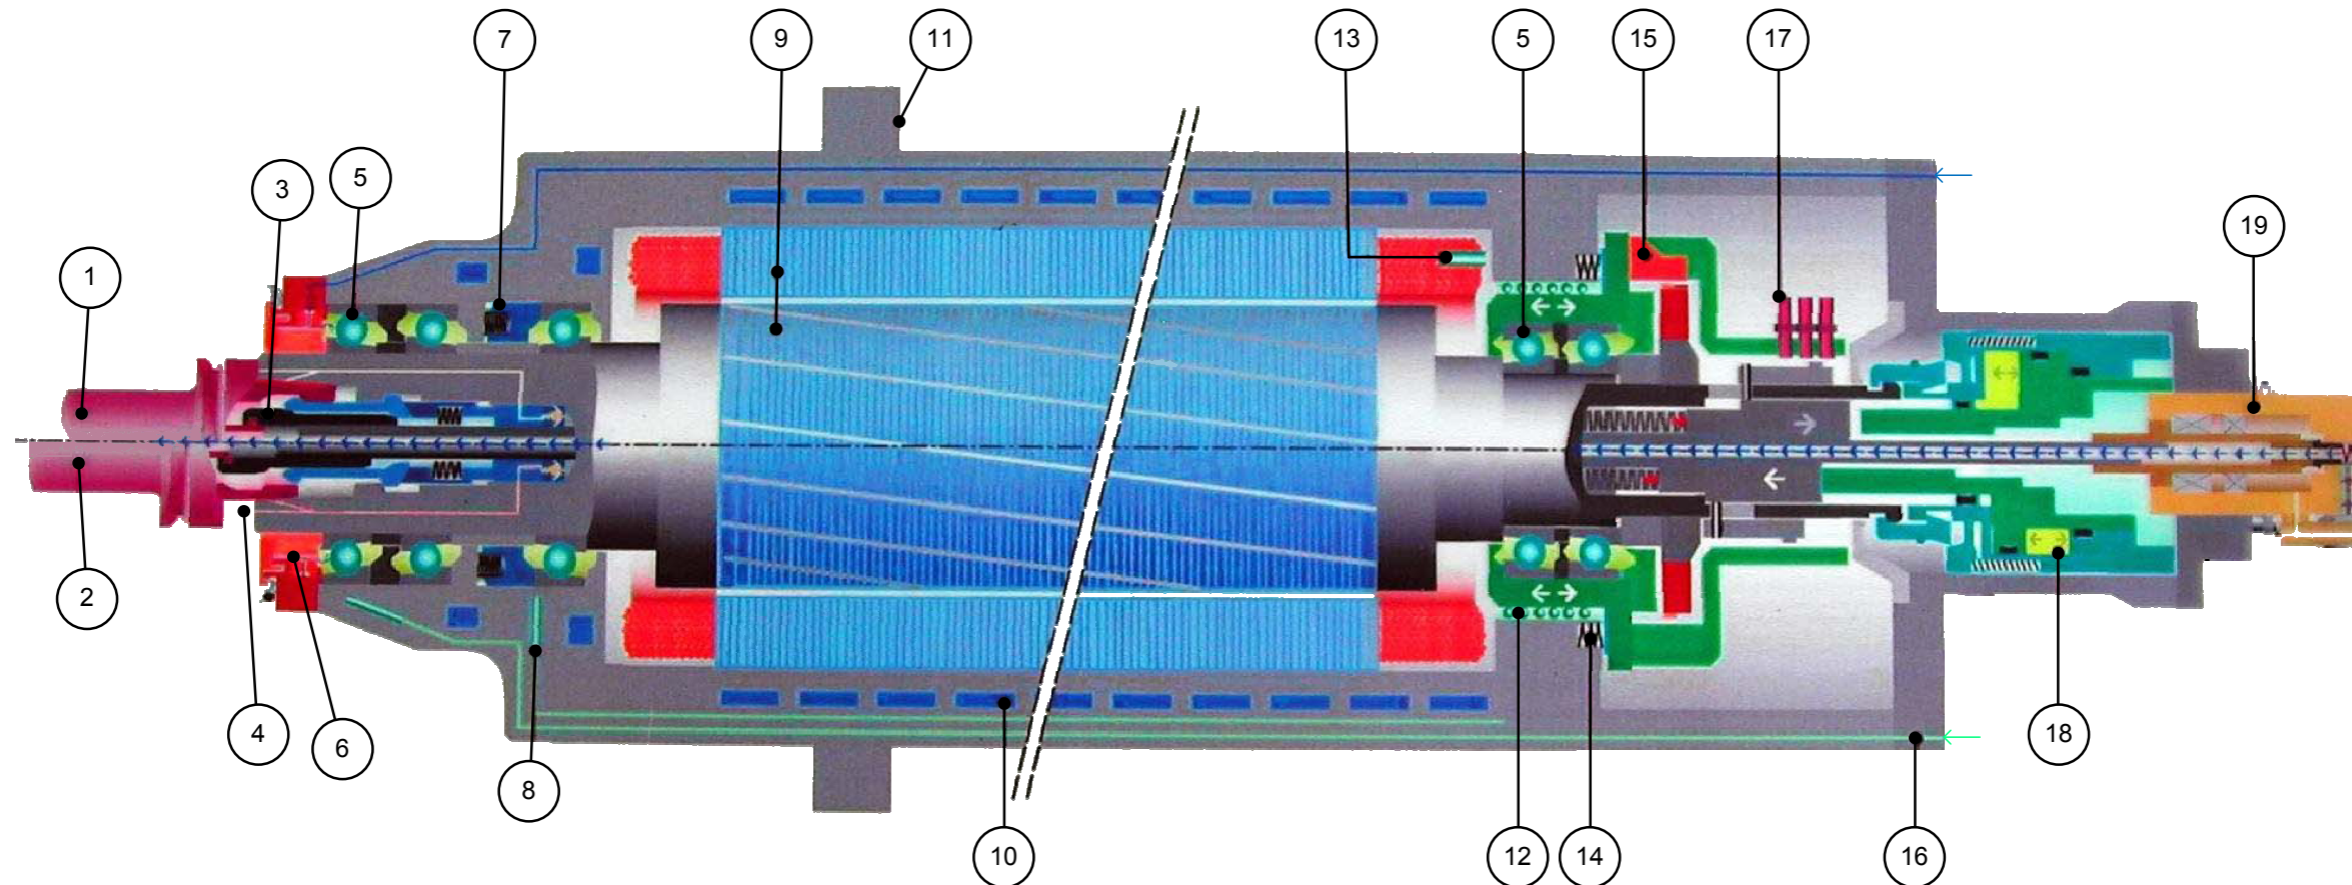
Vue en coupe d'un électrobroche UGV.
